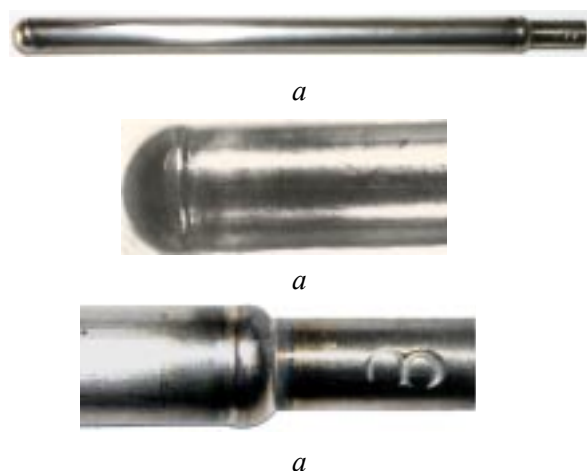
Сталь ЭК-181. Сварные соединения трубчатых образцов диам.6,9×0,4 мм (аргонодуговая сварка, АДС): а – общий вид образца; б – сварной шов типа ДУМП (АДС дугой, управляемой магнитным полем); в – сварной шов периметрического типа.
